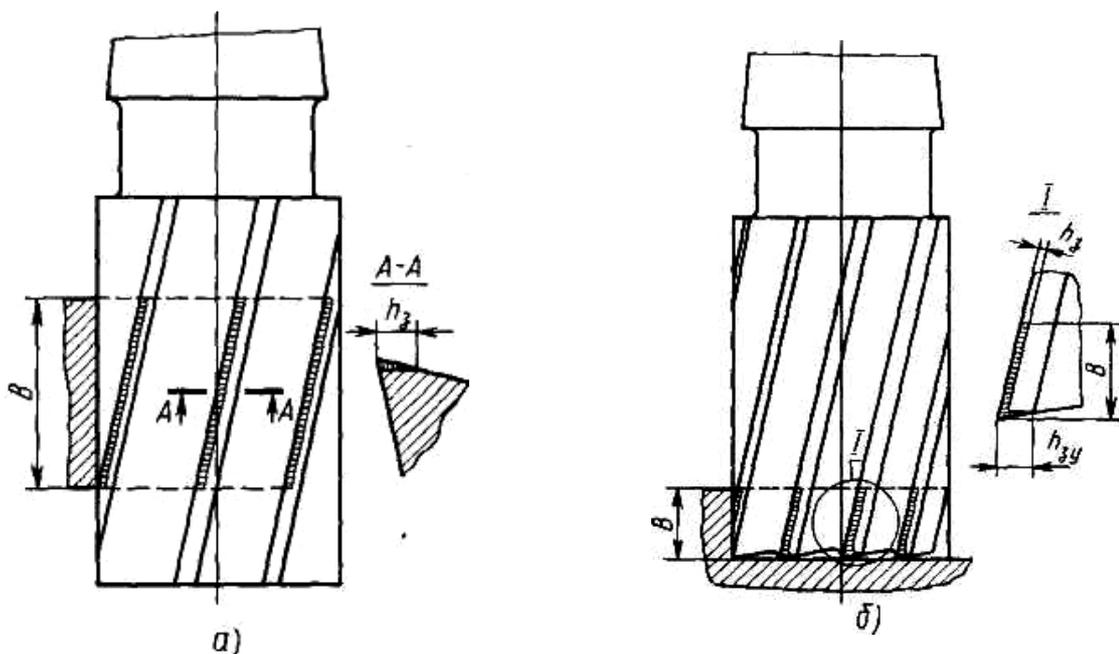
Износ задних поверхностей лезвий зуба фрезы
